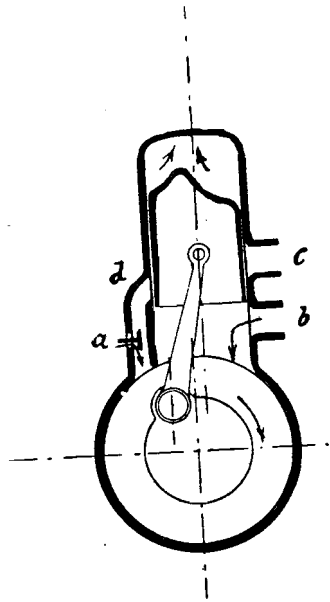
Zweitaktmotor mit selbsttätigem Einlaßventil (Verdichtung des Gasmisches).
